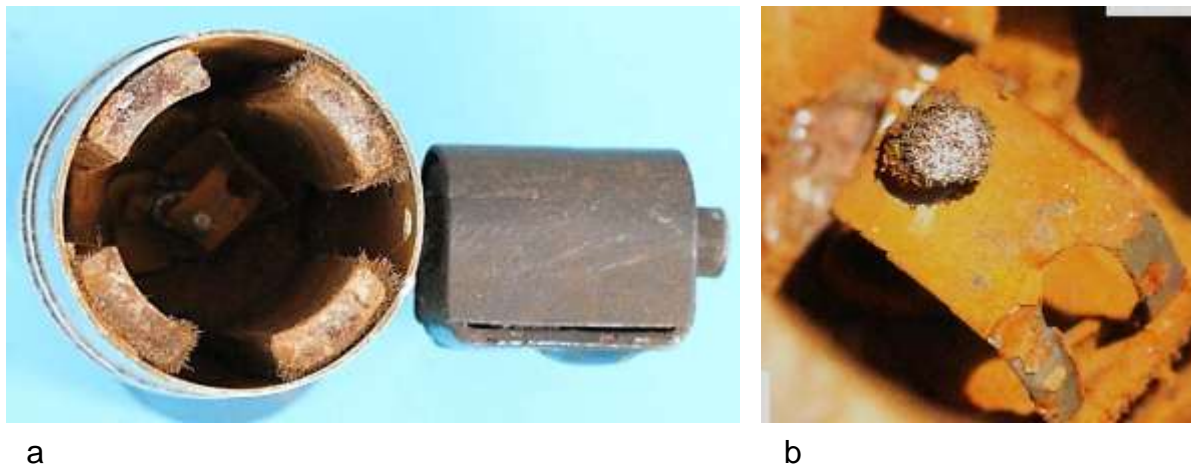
Innenraum des Gehäusemantels: a) Stirnseiten der vier Pole, b) Kupfergewebebürste mit Blattfeder
